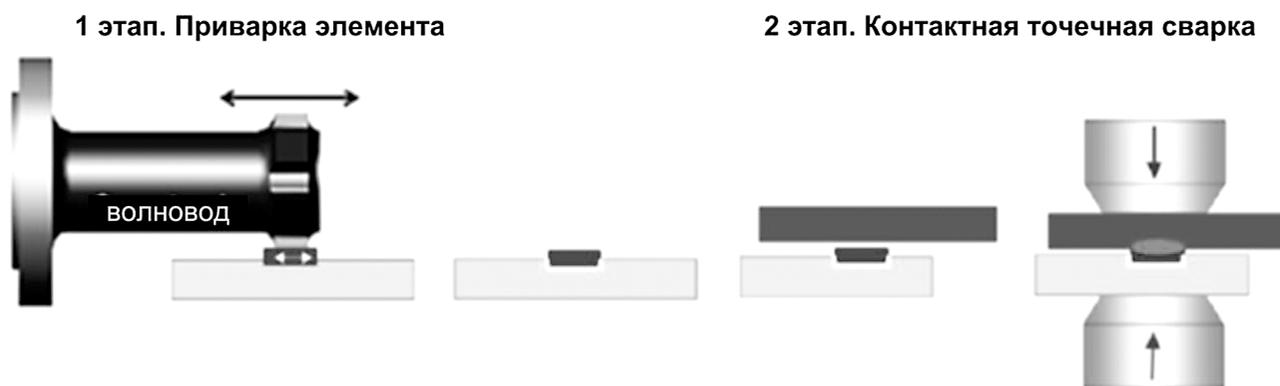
Контактная точечная сварка с внесением вспомогательного элемента при помощи ультразвуковой сварки [6]
